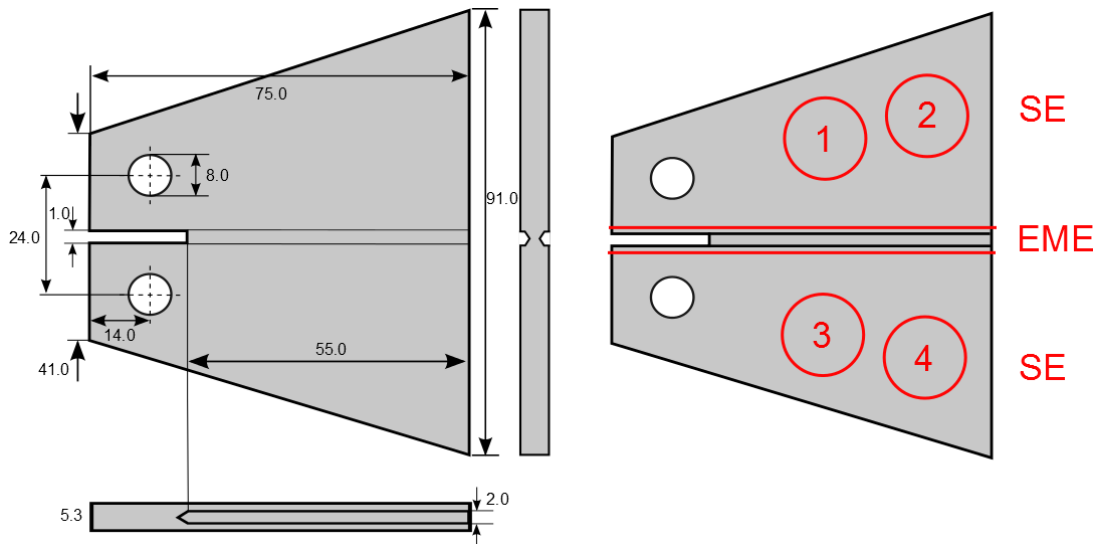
Links: Tensile double cantilever beam (TDCB) Probengeometrie. Rechts: Sensorpositionen.
